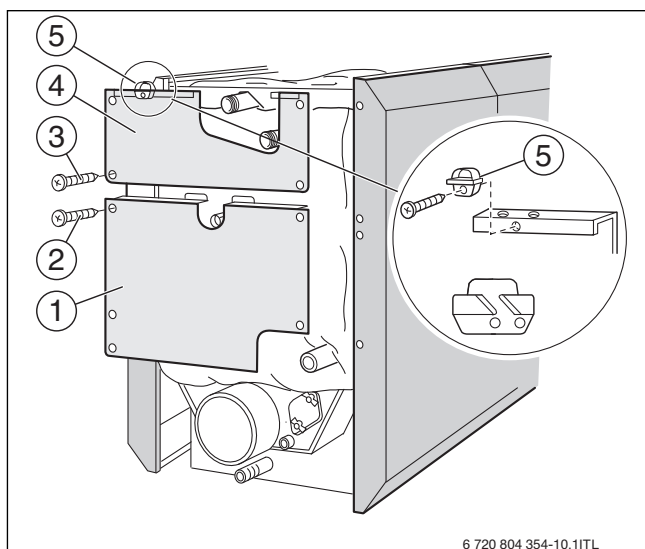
Zavěšení bočních stěn a připevnění kabelu hořáku
